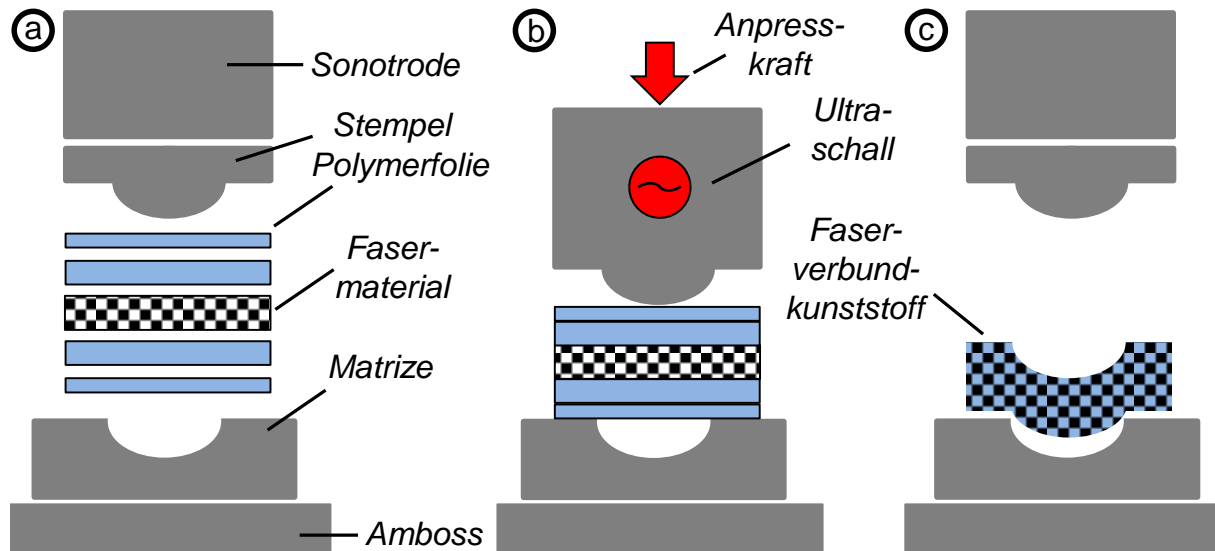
Schematische Darstellung des Schweißwerkzeuges bestehend aus Stempel und Matrize. Das Kugelsegment hat eine Höhe von 4 mm und einen Basiskreis mit einem Durchmesser von 30 mm [13].
